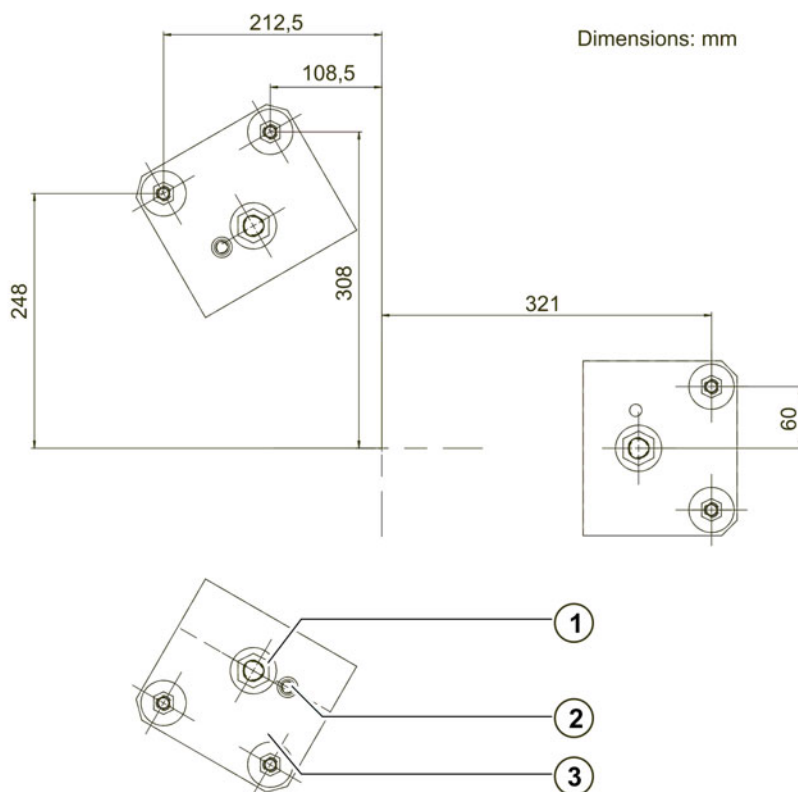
Fixation aux fondations avec centrage, plan coté
